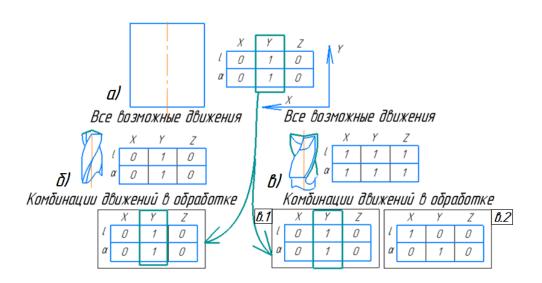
Принцип сопоставления таблиц цилиндрической поверхности (а) с таблицами движений сверла (б) и концевой фрезы (в)
